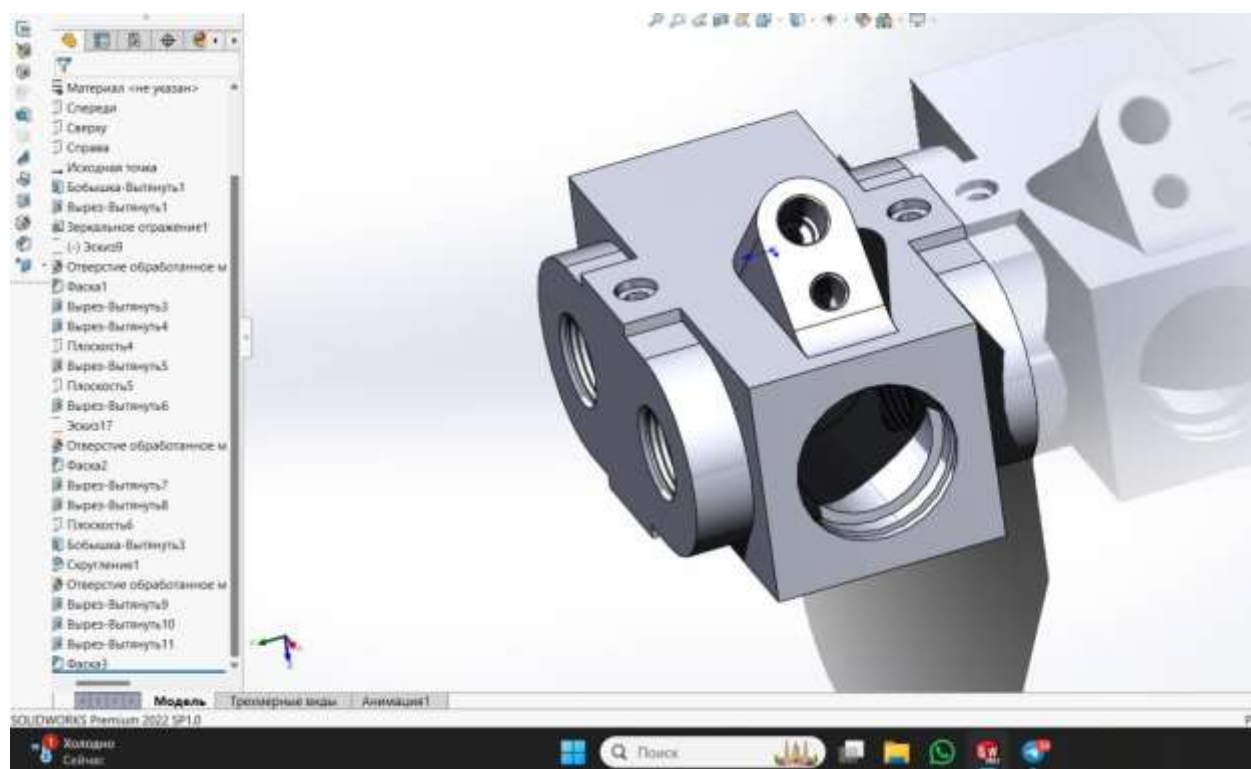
Твердотільна модель деталі Корпус 41.01
